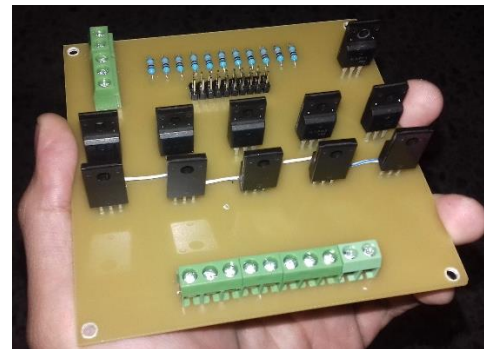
Placa de MOSFETS con elementos soldado
